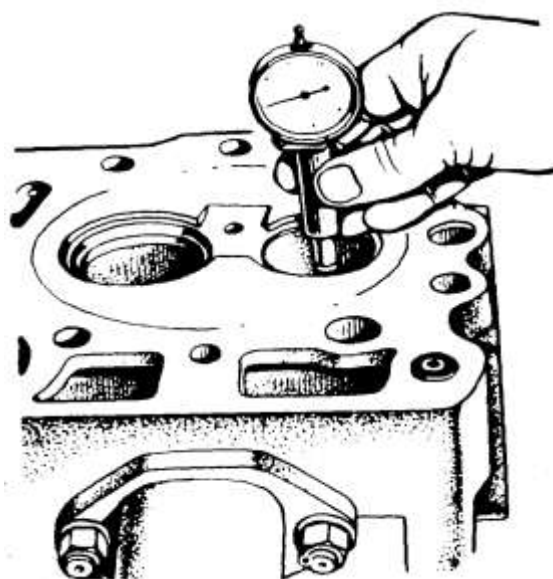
Контроль диаметра направляющей втулки клапана.
